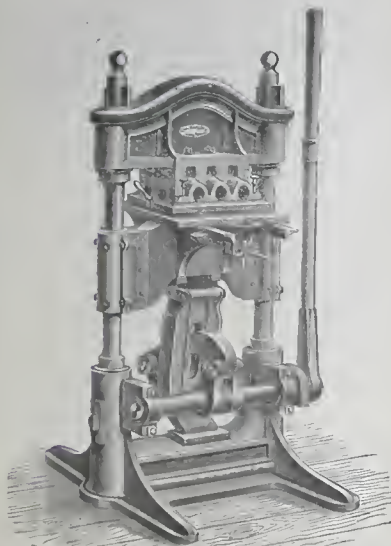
Pressmaschine mit einem Getriebe von Eisen. Stempel in Kupfer-Metall.
